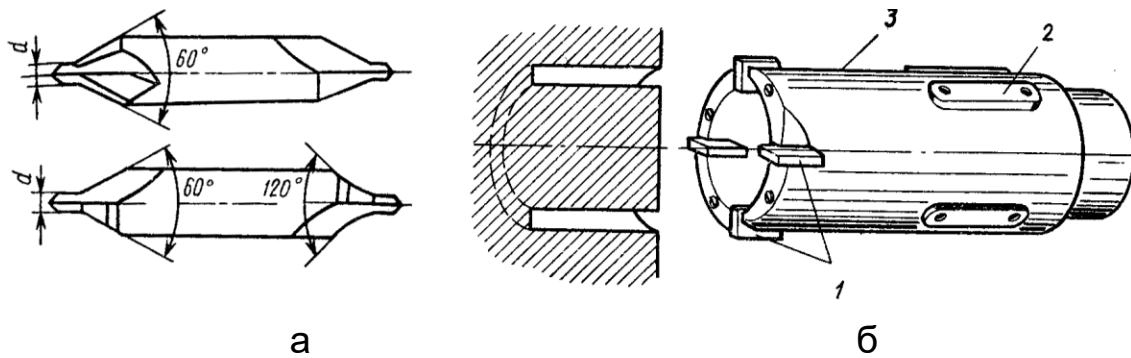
Сверла: а – центровочные; б – кольцевое
